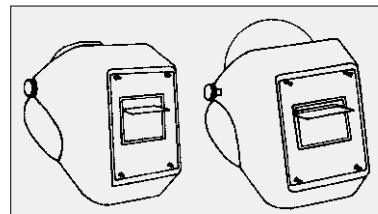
Сварочный щиток с комбинированным светофильтром и козырьком
